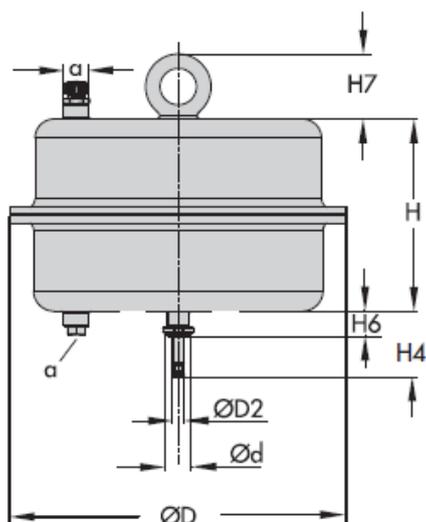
• Тип 3271 Пневматический привод с 1400-60
